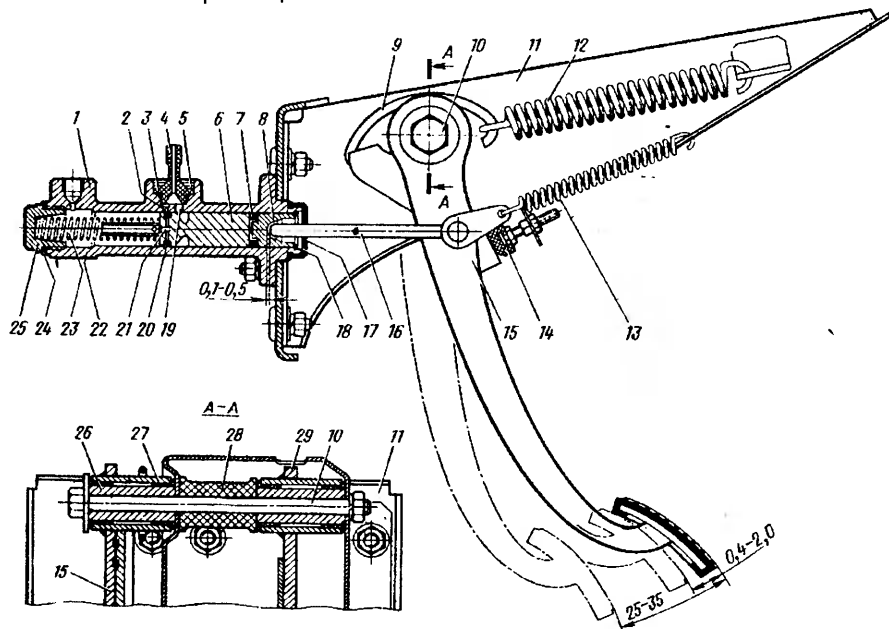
Педаль и главный цилиндр привода выключения сцепления:
